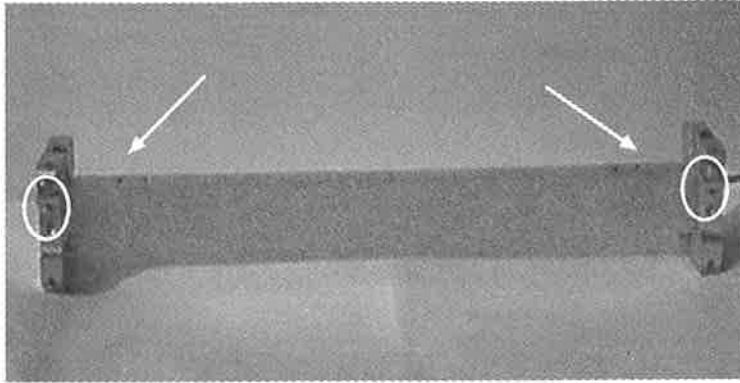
View of carriage assembly.('98. 6.~'99. 5.)
